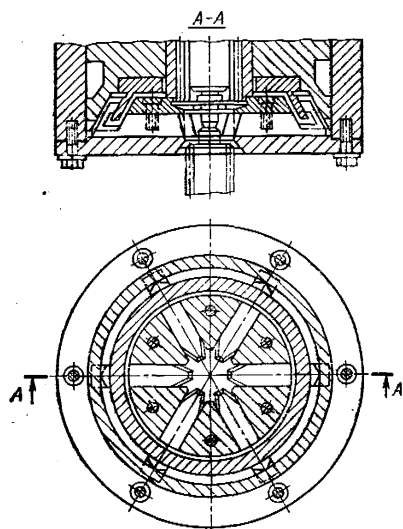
Резцовая головка шлицестрогального станка
